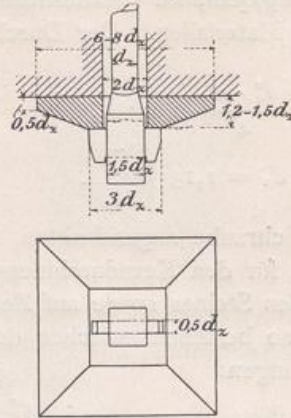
u. 114. Verbindung der Platte mit dem Bolzen durch eine Schraubenmutter.
